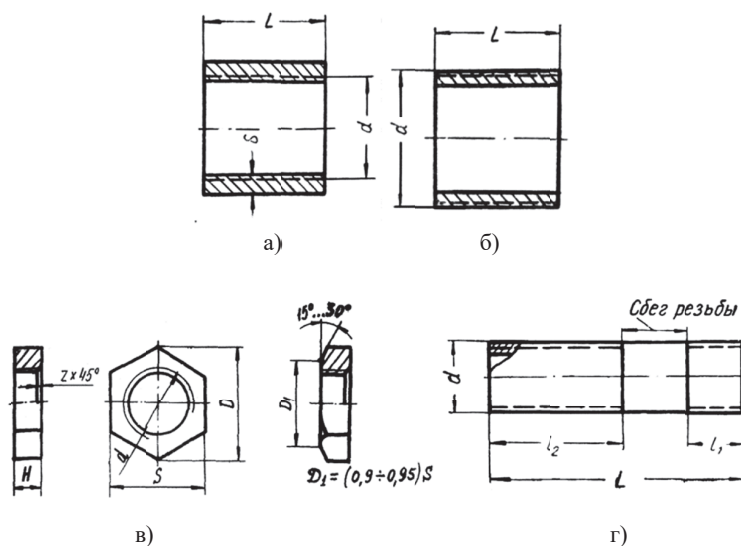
Детали резьбового соединения с трубной цилиндрической резьбой по ГОСТ 6357-81:
